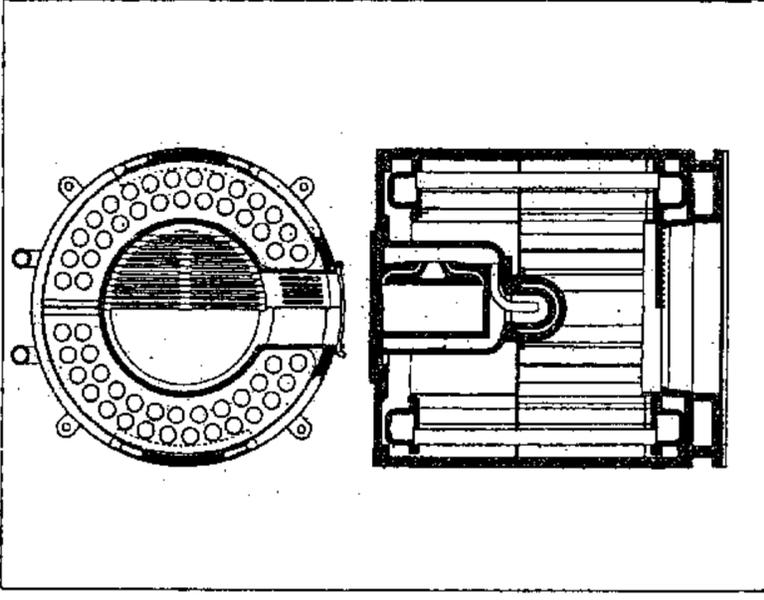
/2: Kessel des „Elze-Dampfmotor“ der Maschinenfabrik von G. A. Kroll & Co (um 1880)
